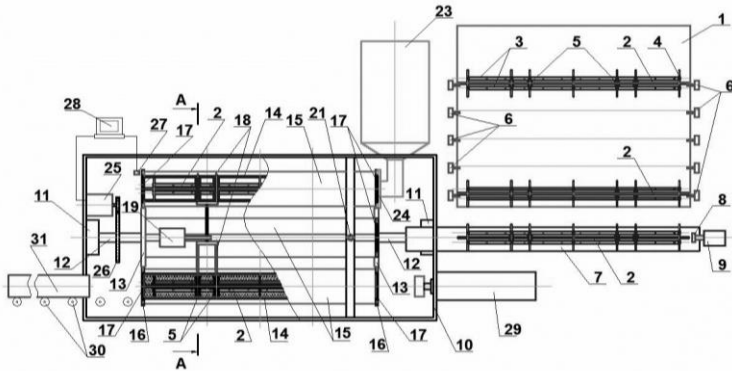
Общая схема устройства для изготовления композиционной шпалы (накопитель 1; армирующая сборка 2; магнитный втулка-маркер 3; позиционирующие эле менты 4; закладный элемент 5; электромагнитная замка 6; желоб-кондуктор 7; толкатель 8; привод 9; жесткая рамная конструкция 10; подшипниковый узел 11; полуось 12; термоизолирующая проставка 13; пресс-формы 14; рубашка теплообменника 15; силовой фланец 16; шиберная заслонка 17; стержни-фиксаторы 18; привод 19; гидроразъемы 20 и 21; трубопровод 22; экструдер 23; разъем 24; привод вращения 25; механическая передача 26; датчик положения 27; ЭВМ 28; толкатель 29; рольганг 30; готовая шпала 31)
